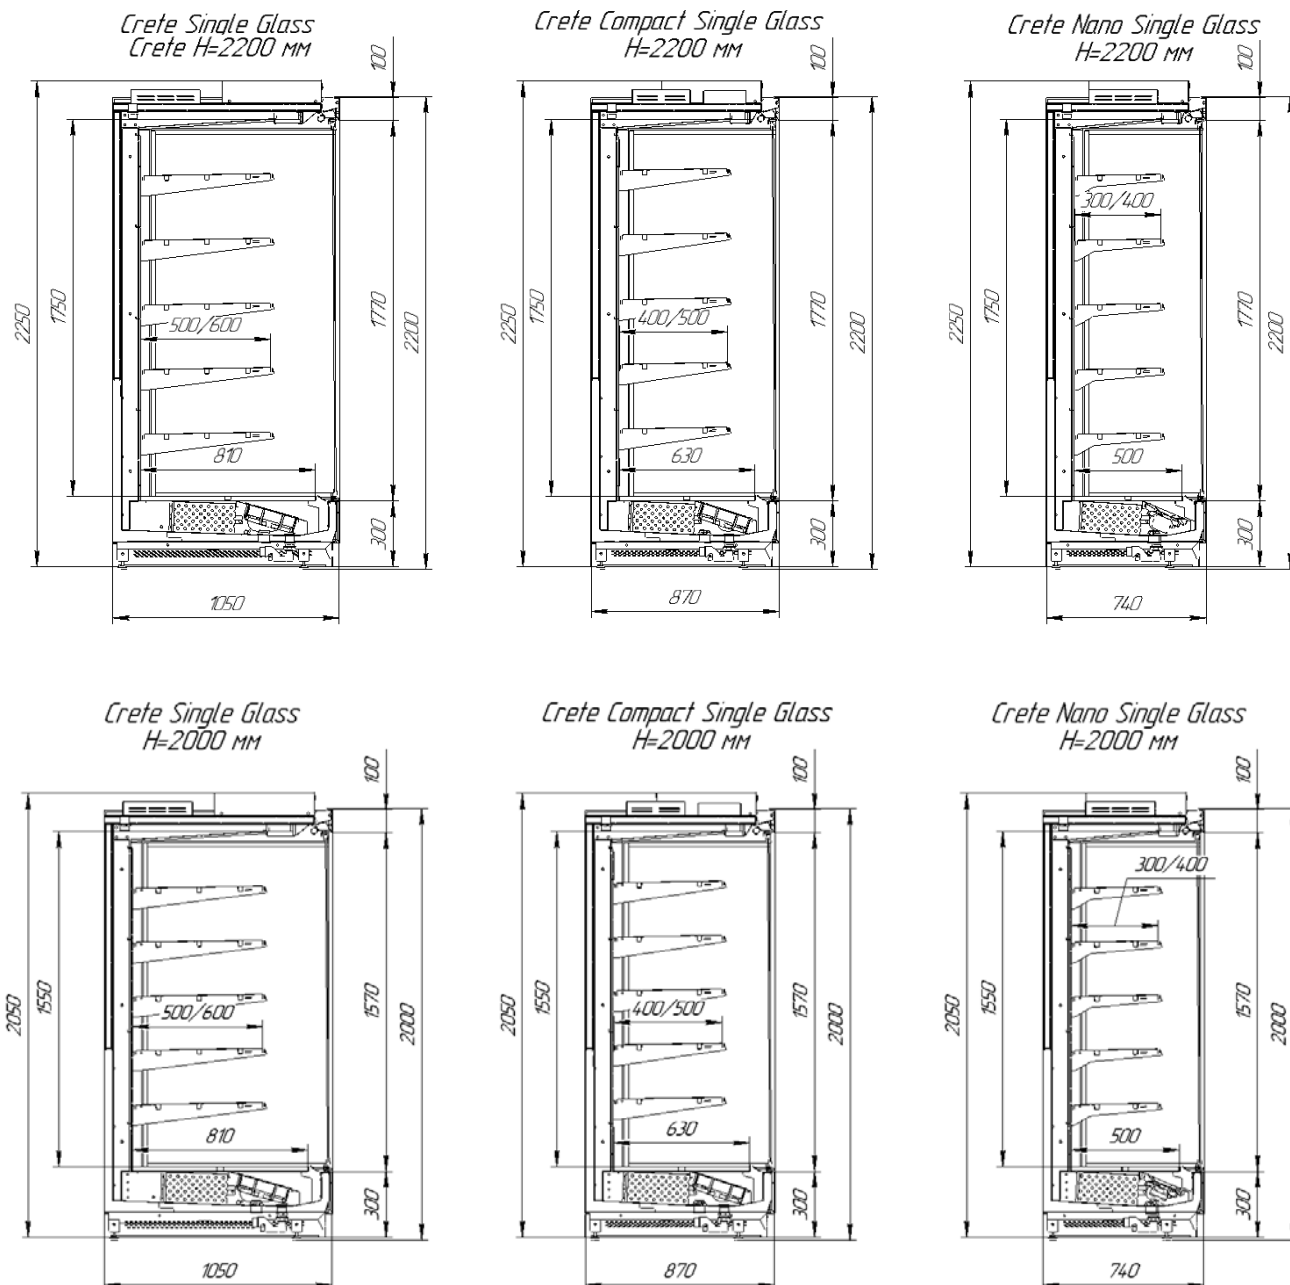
Сечение витрины Crete/Crete Compact/Crete Nano Single Glass
